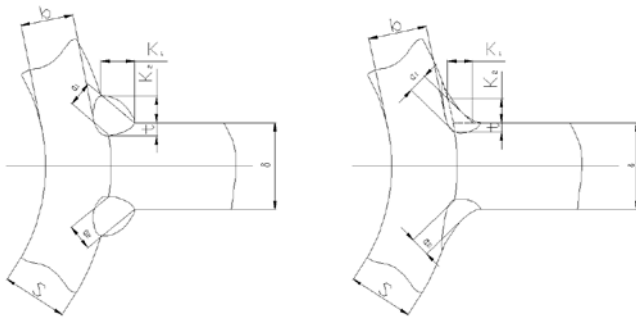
气体保护焊、焊条电弧焊钢管与扁钢焊接熔深要求
